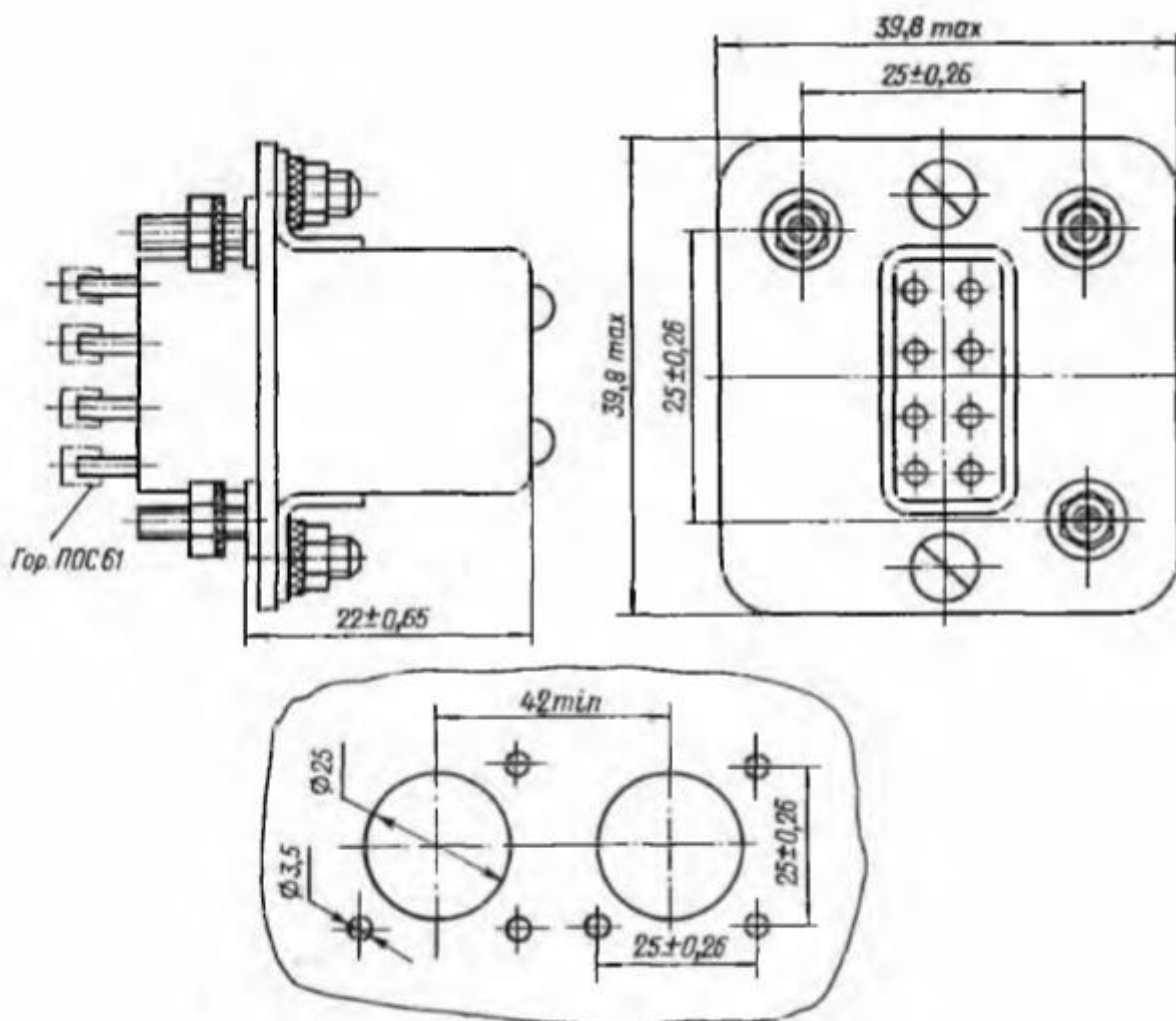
Конструктивные данные реле РЭС59В (с платой для болтового крепления) и разметка для крепления
